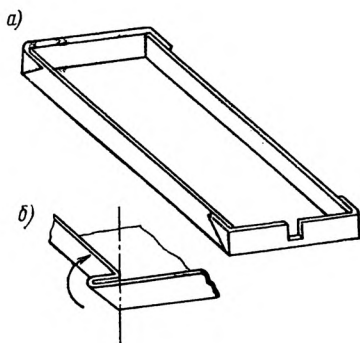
Изложница типа подноса для отливки плоских нерастворимых анодов из свинца или свинцового сплава: а — общий вид, б — способ загиба угла
